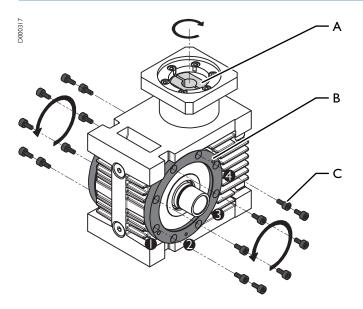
Getriebespiel einstellen: Getriebeeinheit Güdel
